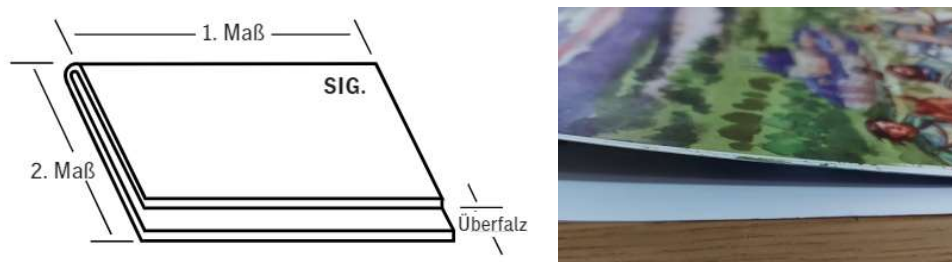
Fălțuire cu supradimensionare de minim 5 mm
